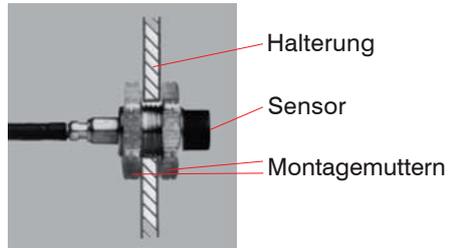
Ungeschirmter Sensor mit Gewinde in Standardmontage
